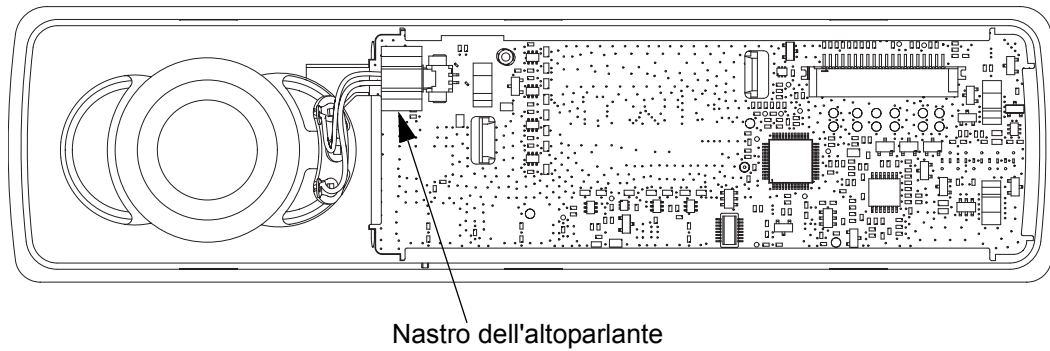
Montaggio del nastro dell'altoparlante sul PCB
